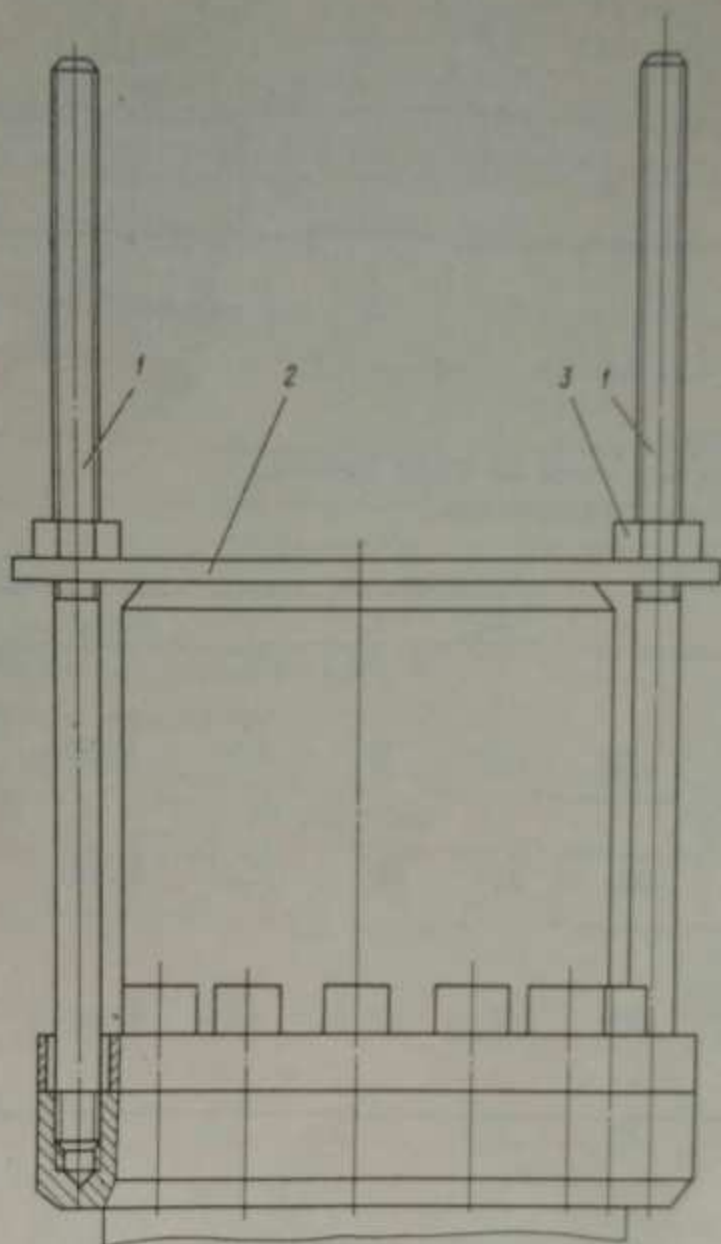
Приспособление для разборки и сборки клапана в наполнении:
